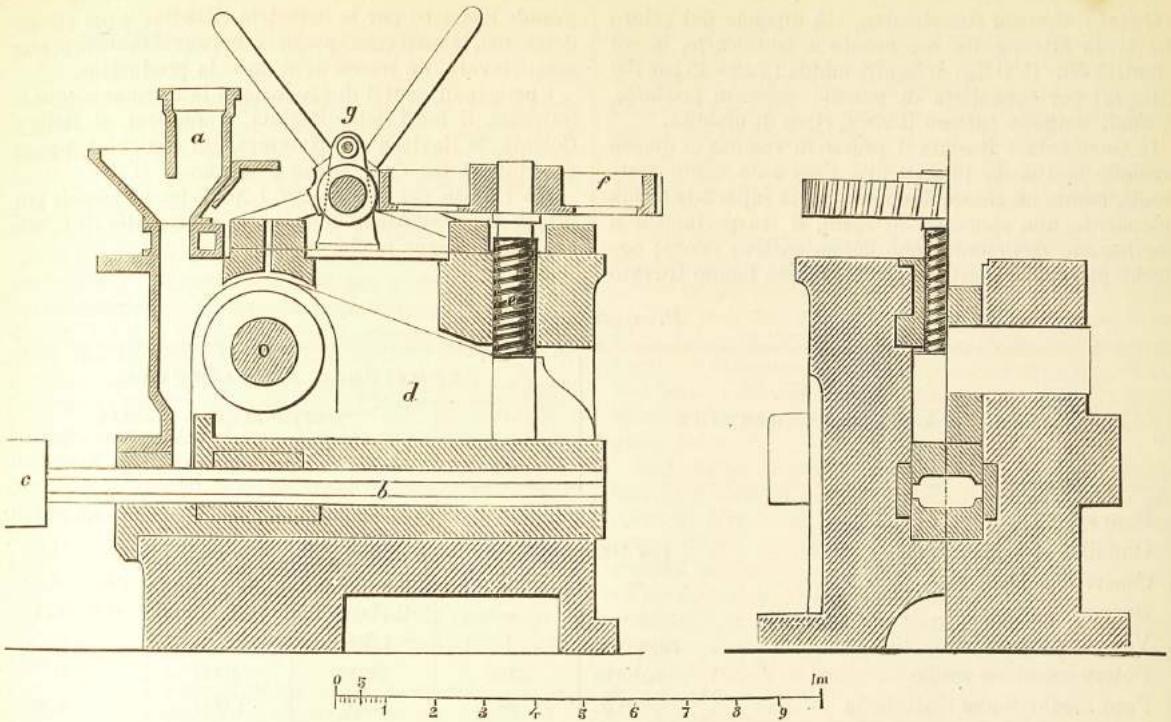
Macchina Exter per mattonelle di lignite.
